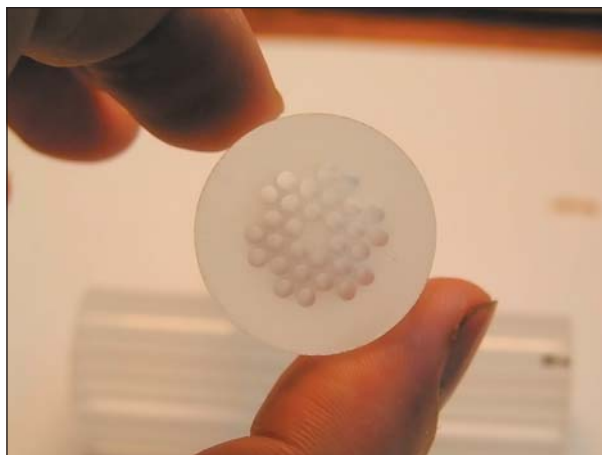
Установка для сверления и заготовка из плавленного кварца для вытяжки фотонно-кристаллического волокна.
